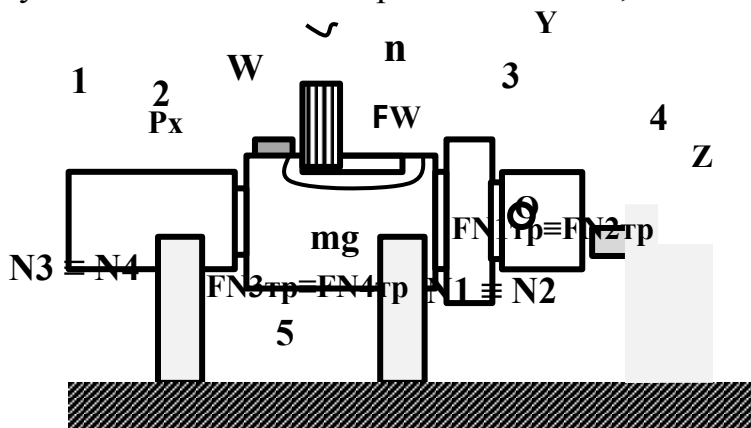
Силы, действующие на деталь в процессе фрезерования шпоночного паза.
